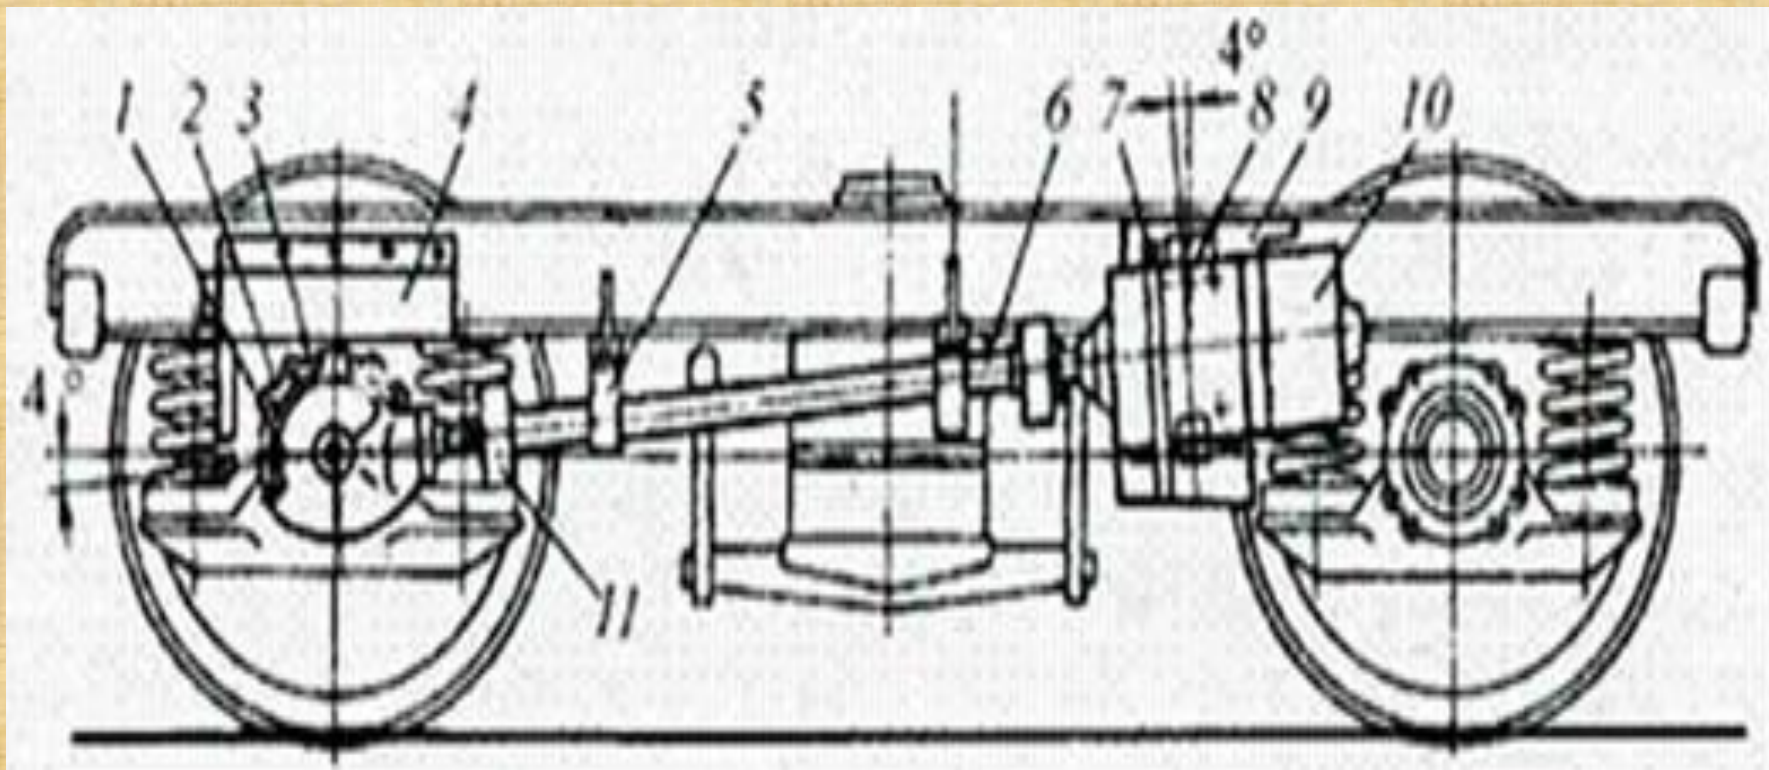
Редукторно-карданный привод генератора, установленный на тележке: 1 – редуктор; 2 – промежуточное кольцо, прикрепленное болтами к корпусу; 3 – предохранительная скоба для редуктора; 4 – влагозащитное устройство, недопускающее попадания влаги на редуктор; 5 – предохранительная скоба для приводного вала; 6 – приводной карданный вал; 7 – хомут для генератора; 8 – предохранительная скоба для генератора; 9 – плита крепления генератора; 10 – генератор вала и генератора.
